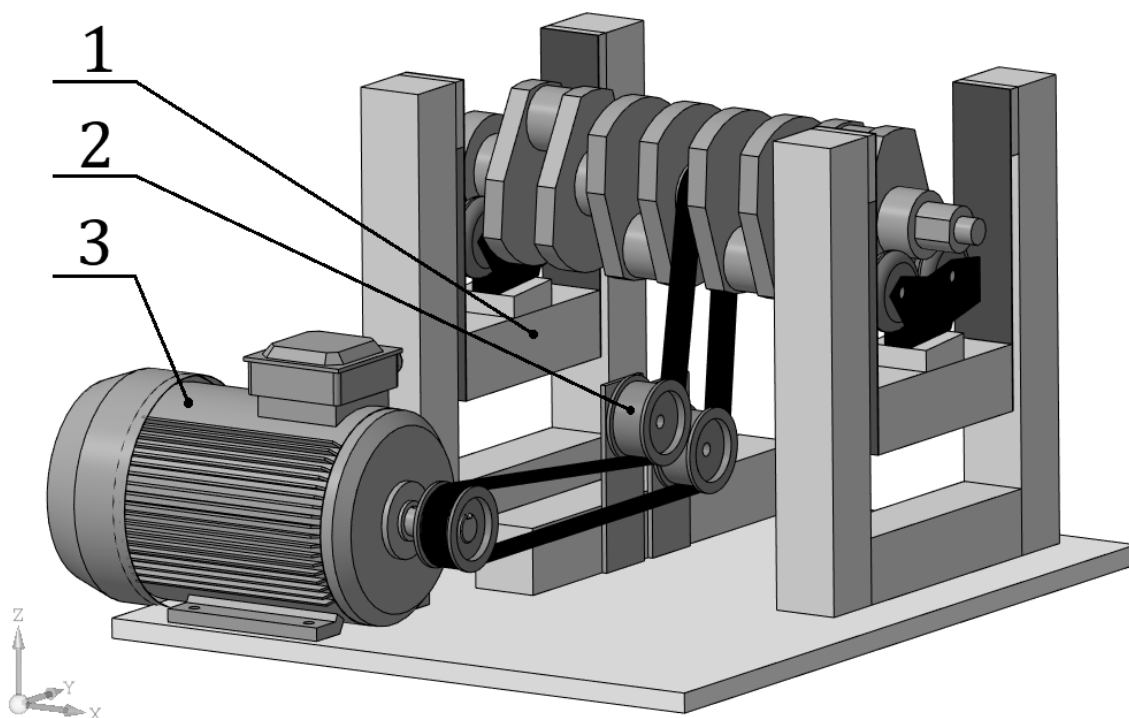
Трехмерная модель прототипа балансировочного станда: 1 – Подвесная опора с роликами; 2 – механизм натяжения приводного ремня; 3 – электродвигатель АИР80В6
